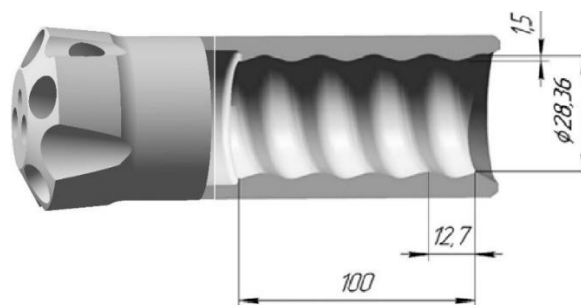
Корпус бурової коронки з різьбовою частиною R32 ISO 10208
